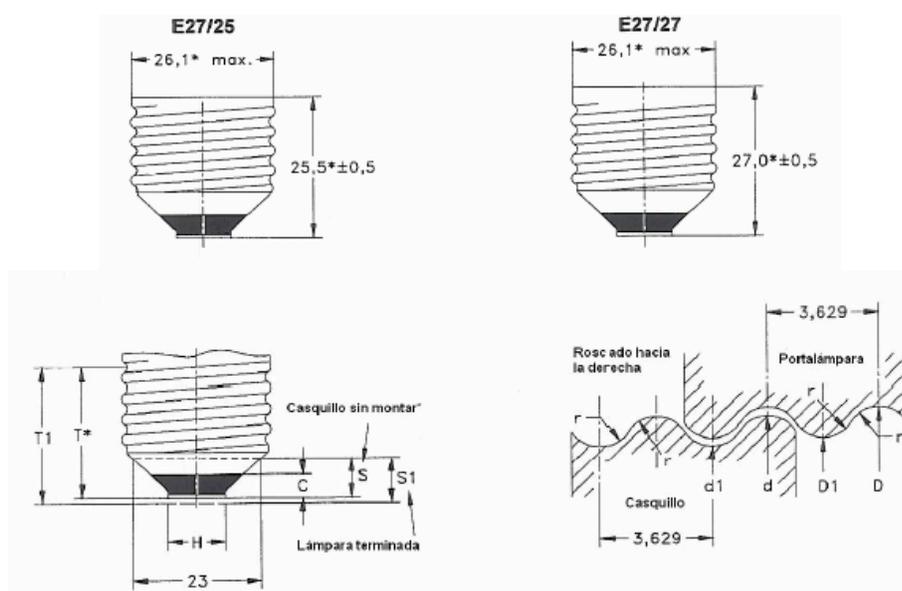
Dimensiones del casquillo de una bombilla en milímetros.
